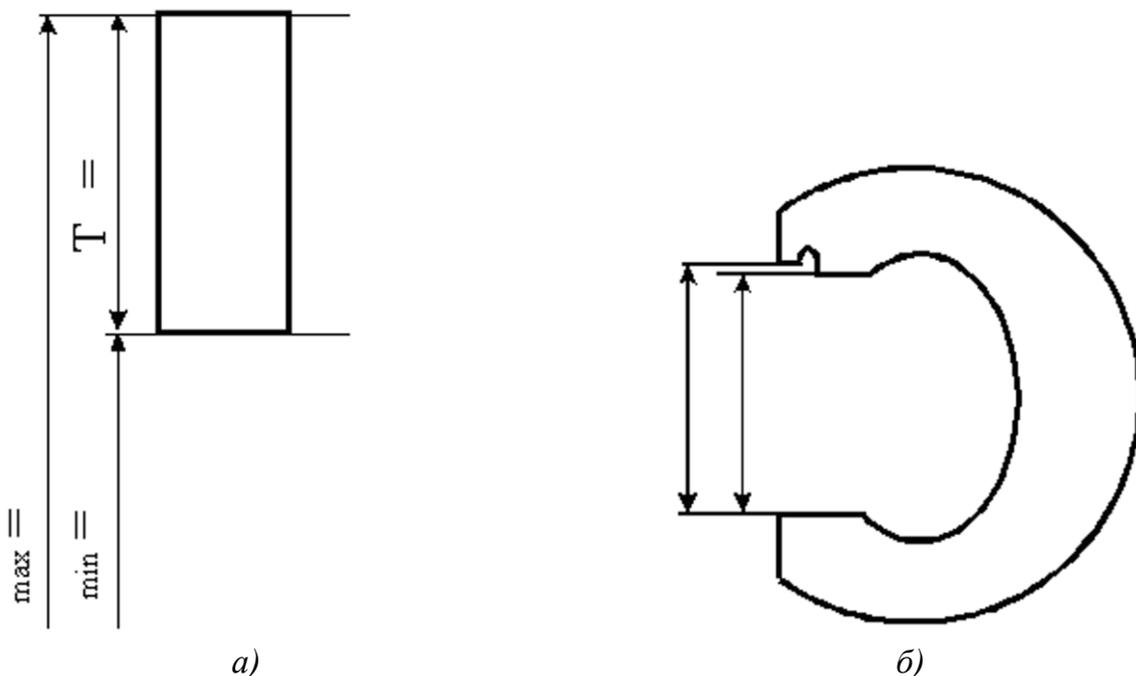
Схема полей допусков (а) и эскиз калибра-скобы (б)
